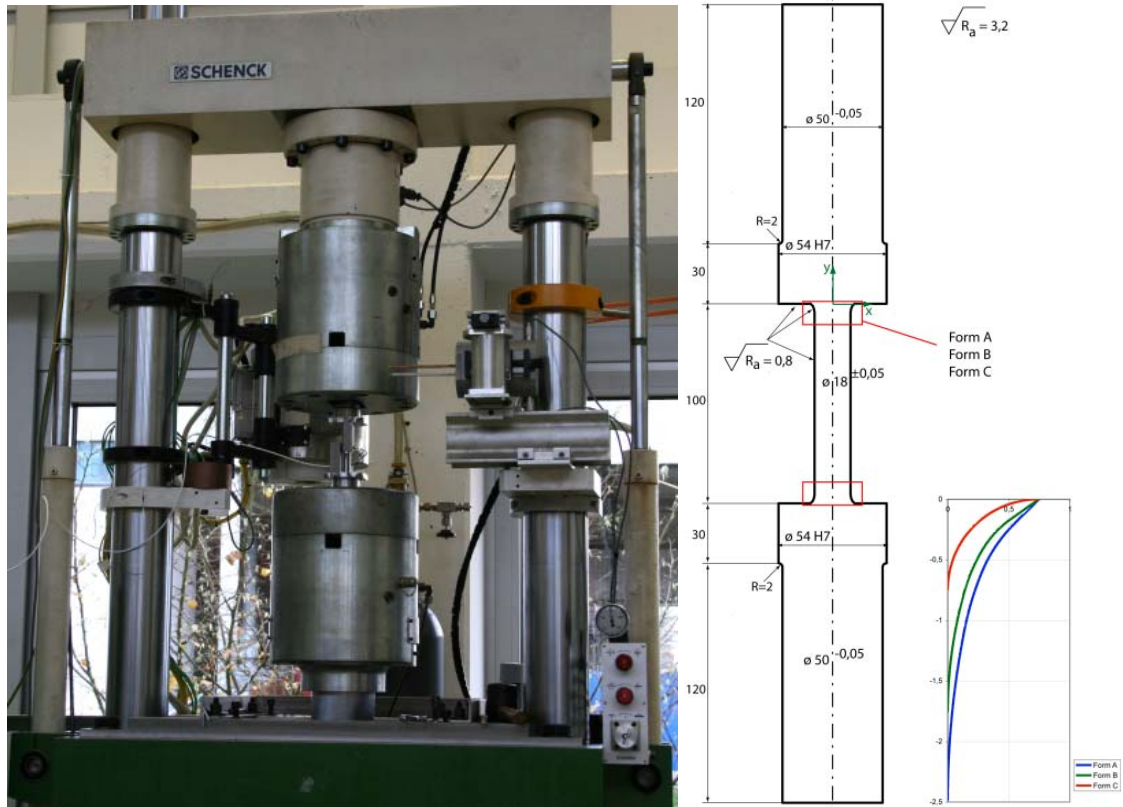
Torsionsprüfmaschine und Zeichnung der Torsionsproben.
